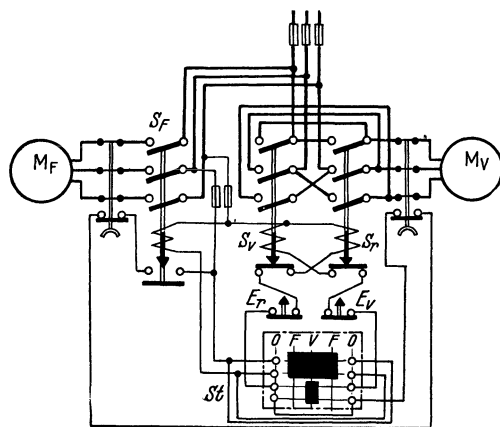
Fräsmaschinensteuerung mit Vorschubverriegelung.
